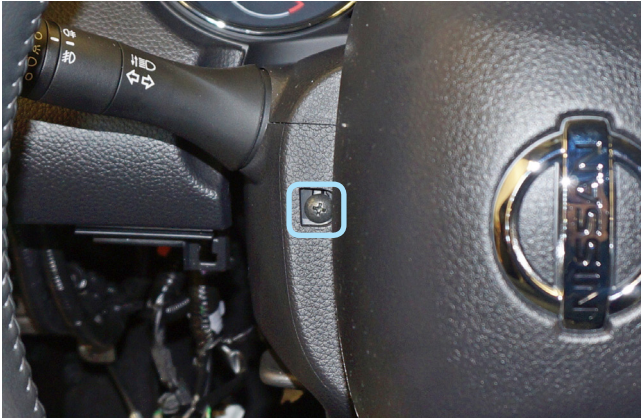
Саморез крепления кожуха рулевого вала слева
